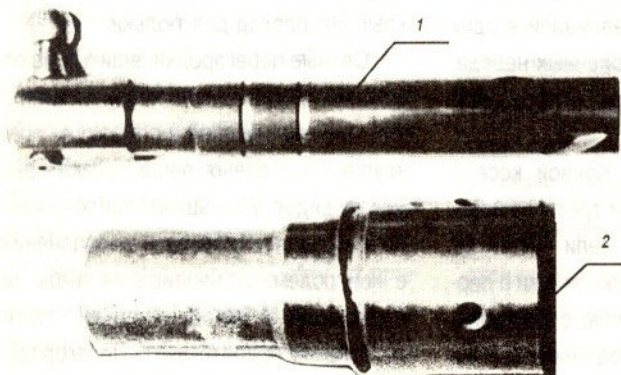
Детали плунжерной пары: 1 – плунжер; 2 – корпус
